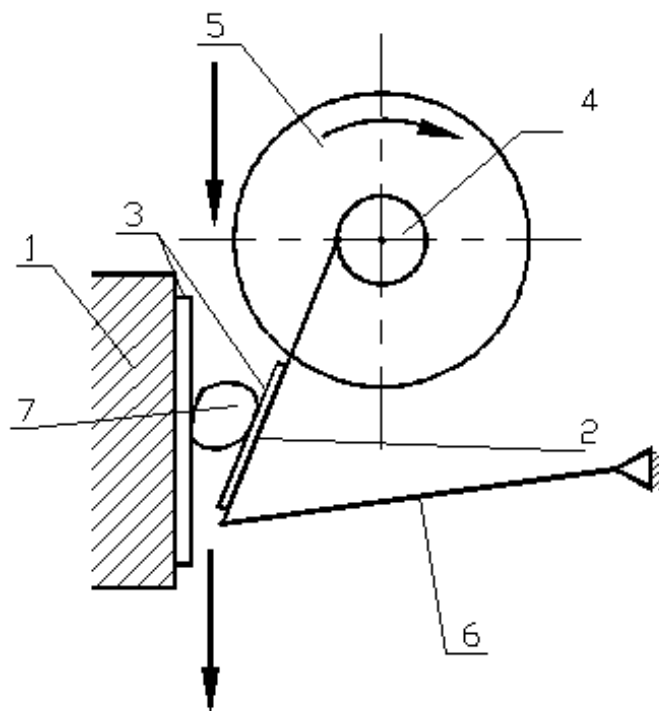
Схема щековой дробилки со сложным качением щеки:
